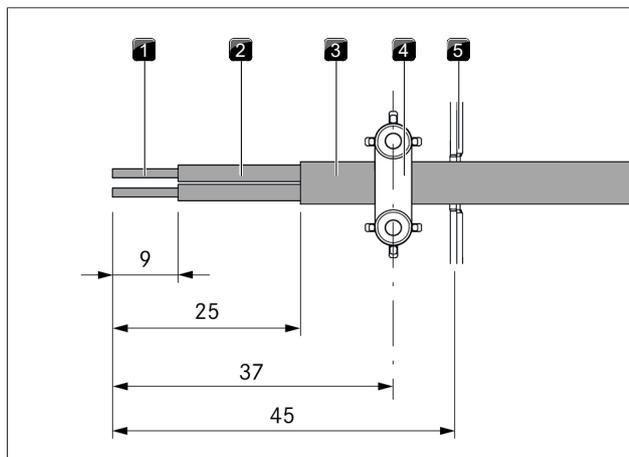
Longitudes peladas y posición de montaje del cable de conexión
